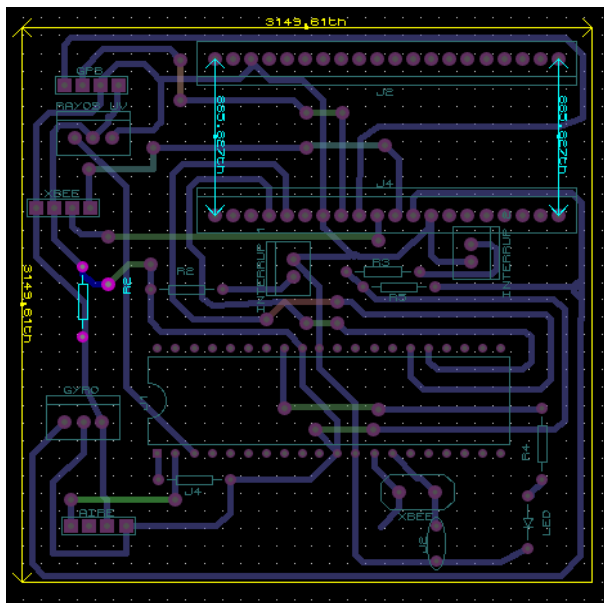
Diseño de PCB para sistema de monitoreo ambiental.
